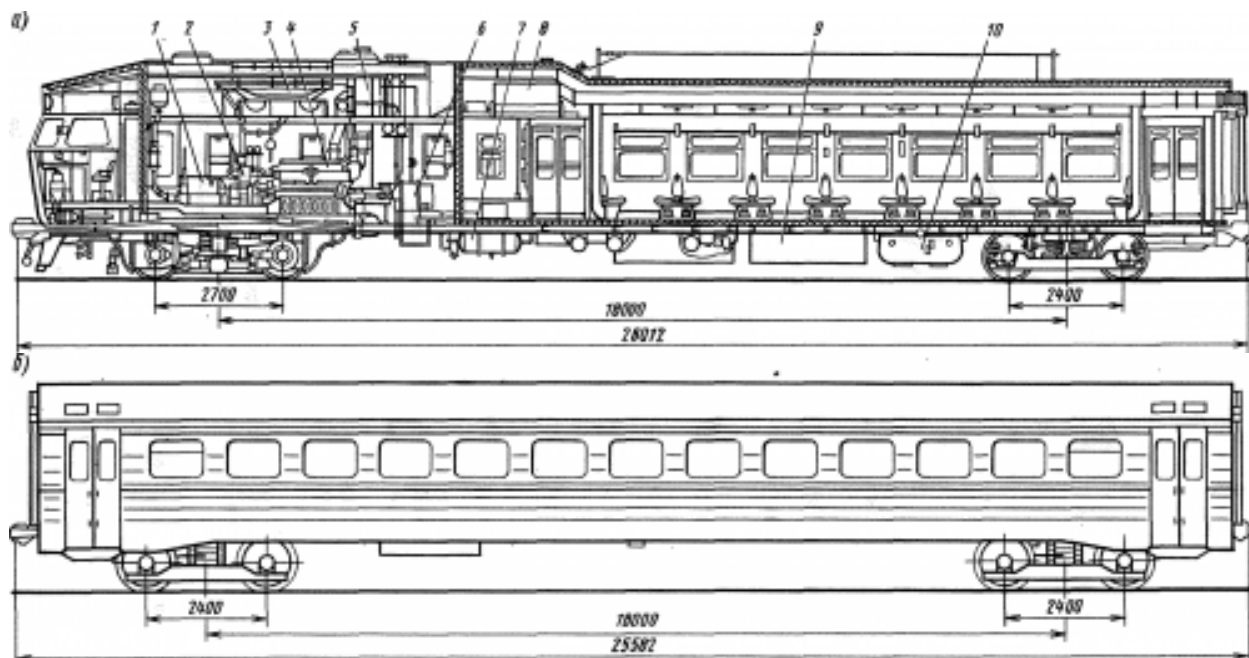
Расположение оборудования и основные размеры моторного (а) и прицепного (б) вагонов дизель-поезда ДР1А:
